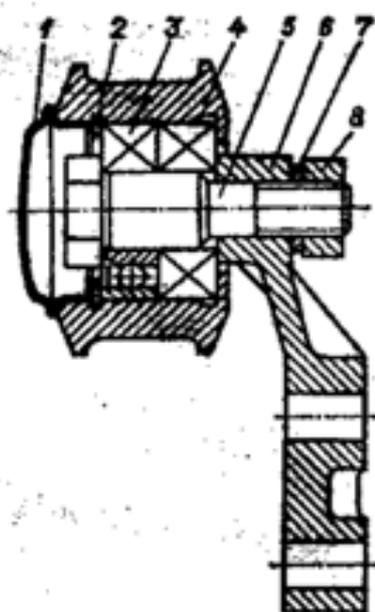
Ролик натяжной: 1 - заглушка; 2 - кольцо стопорное; 3 - подшипник; 4 - ролик; 5 - ось; 6 - кронштейн; 7 - шайба; 8 - гайка
